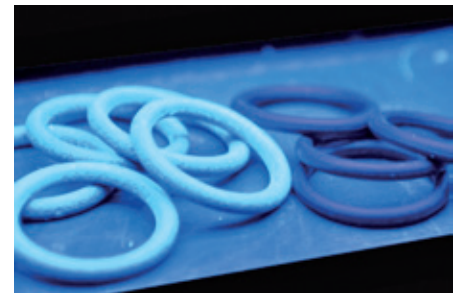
O-Ringe links beschichtet mit Lack mit UV-Indikator, rechts unbeschichtet
